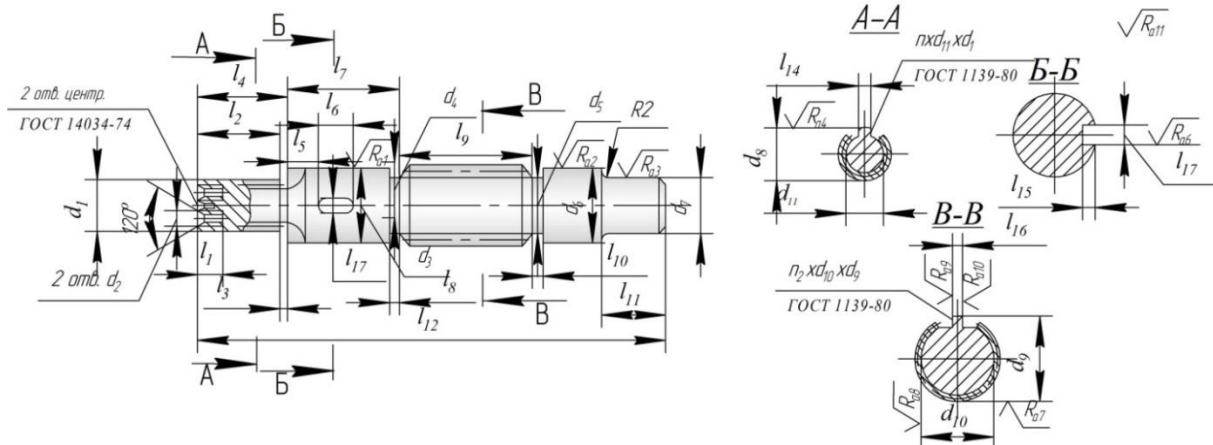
Чертеж комплексной детали «Вал шлицевой».
